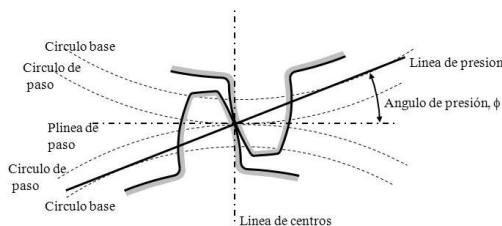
Esquema ángulo de presión engranajes rectos (fuente: HALvarez)
